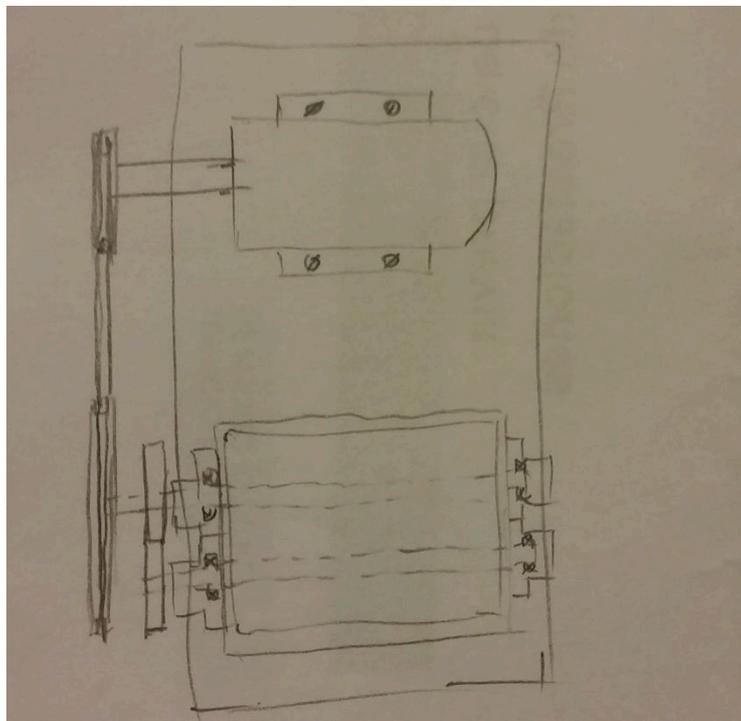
Vista de planta de los elementos de la trituradora colocados en la mesa.
